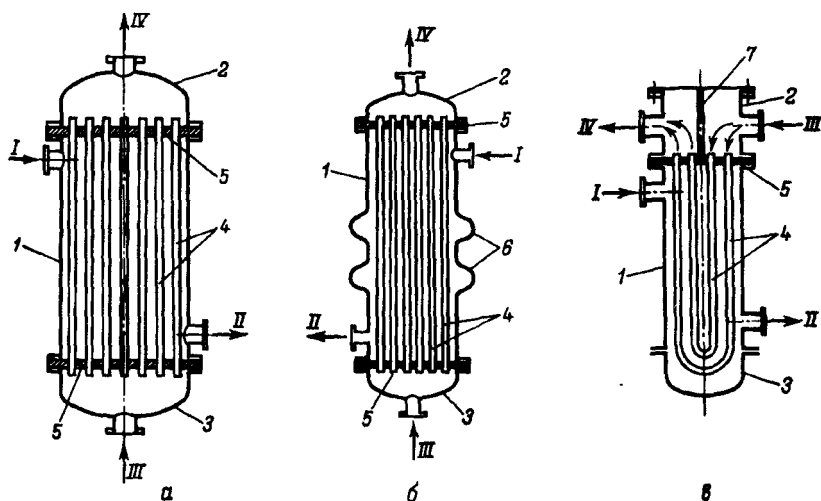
Кожухотрубчатые теплообменные аппараты с неподвижными трубными решетками:
